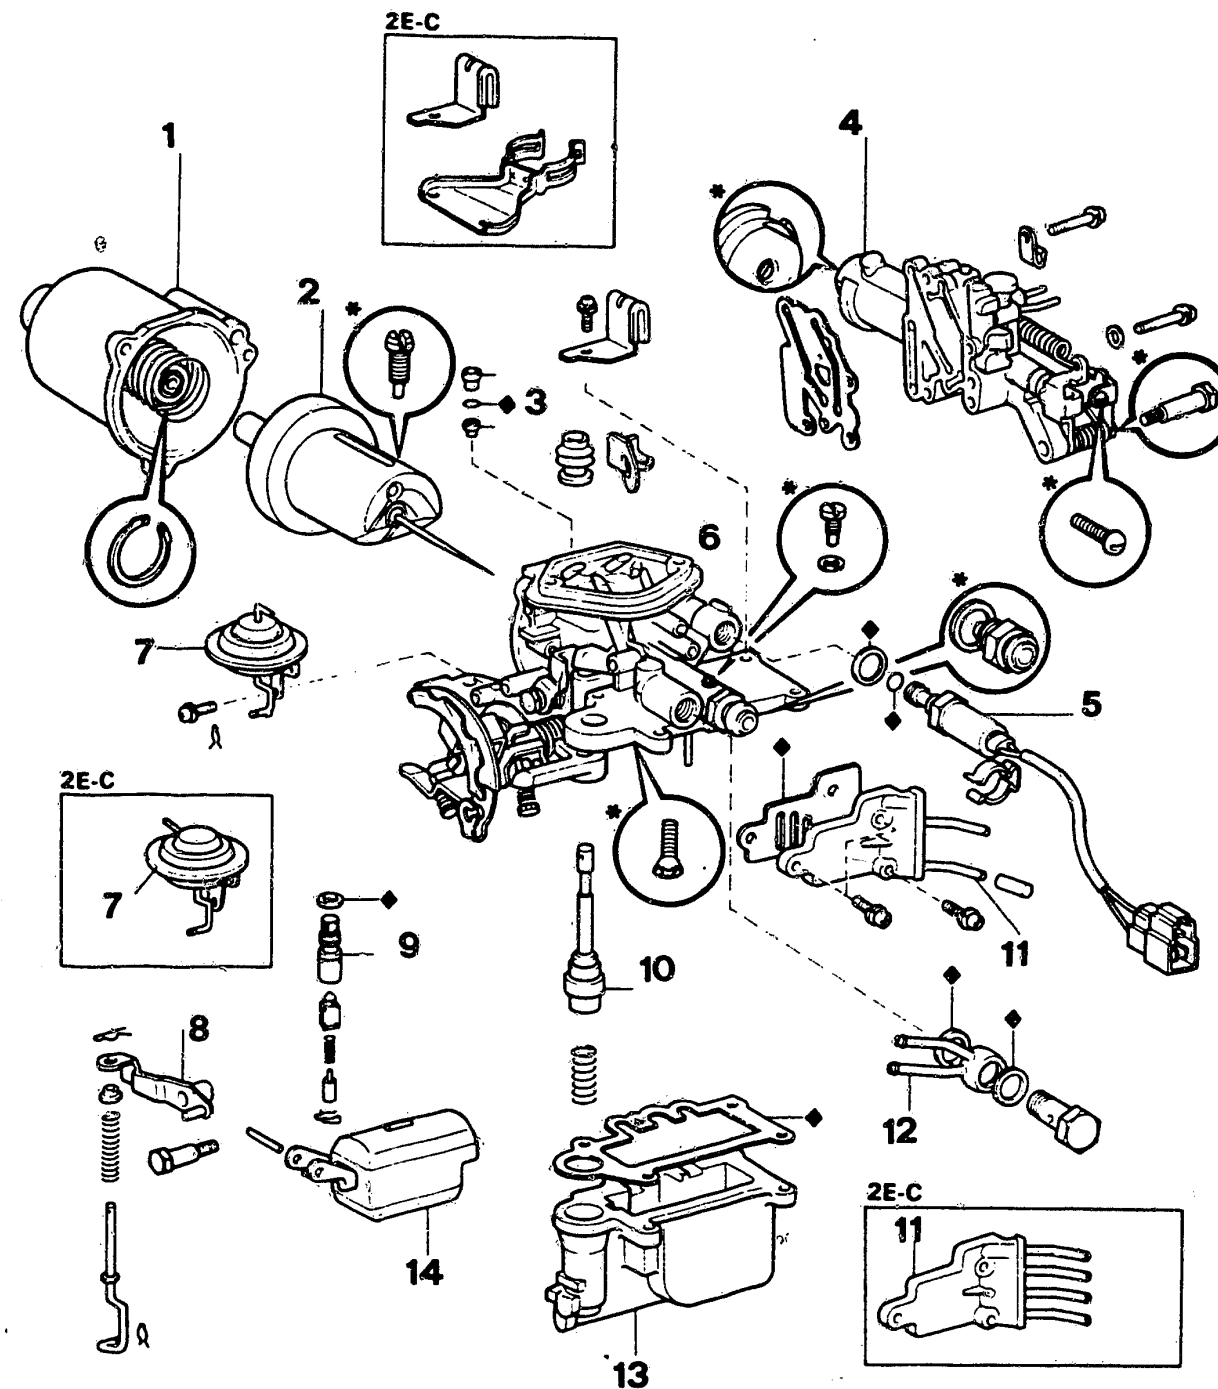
Die wichtigsten Einzelteile des neuen Toyota V-Vergasers: 1 Gehäuse des Luftschiebers – 2 Luftschieber – 3 Führungsbölgchen – 4 Kaltstartkompensator – 5 Leerlauf-Abschaltventil – 6 Hauptgehäuse – 7 Dash-pot = Drosselklappenverzögerer – 8 Pumpenhebel – 9 Schwimmernadelventil – 10 Beschleunigerpumpenkolben – 11 Unterdruckabnahme – 12 Benzinzufuhr- und Rücklaufnippel – 13 Schwimmergehäuse – 14 Schwimmer. ◆ = Teile, die bei jeder Demontage ersetzt werden sollen. * = Teile, die nicht verstellt werden sollen.
